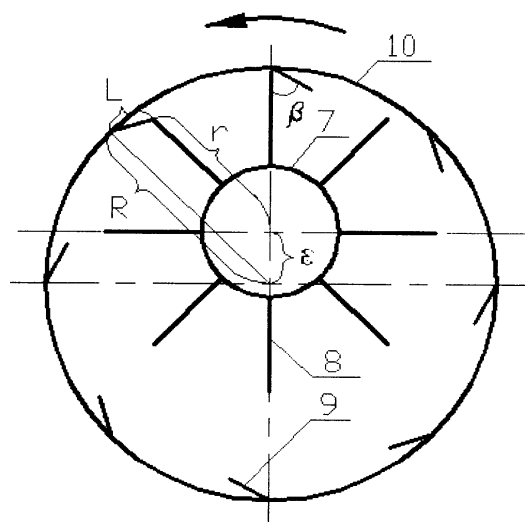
Жидкостнокольцевой вакуумный насос с вращающимся корпусом:
